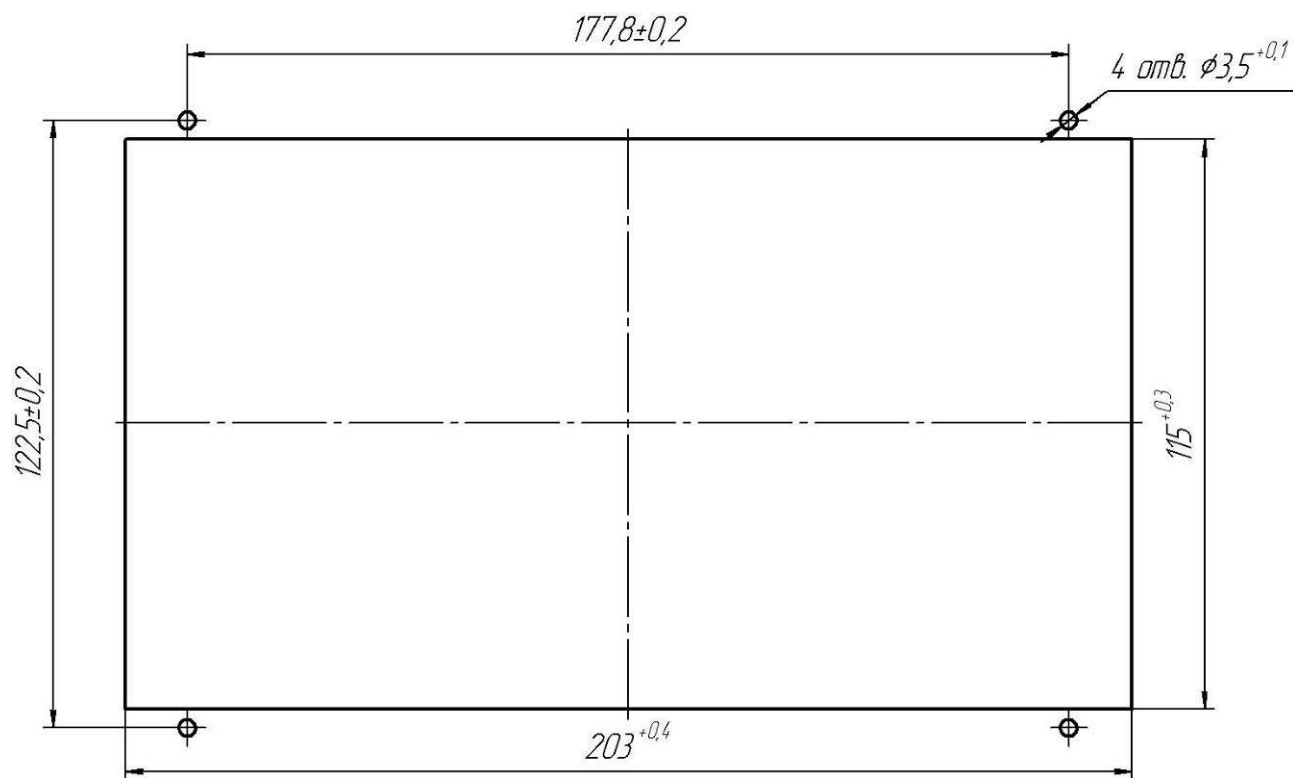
Установочные размеры для установки выносного пульта изнутри шкафа для устройства БЭМП 1-XX.X.(21...32).XXXX.X
